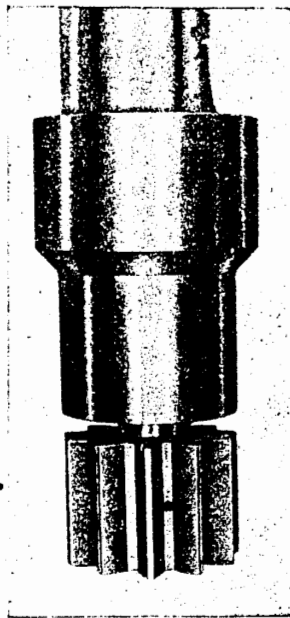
Eindringen der Buchse in das Ölpumpenrad (Werkzeug Nr. 324.020-M 141)
